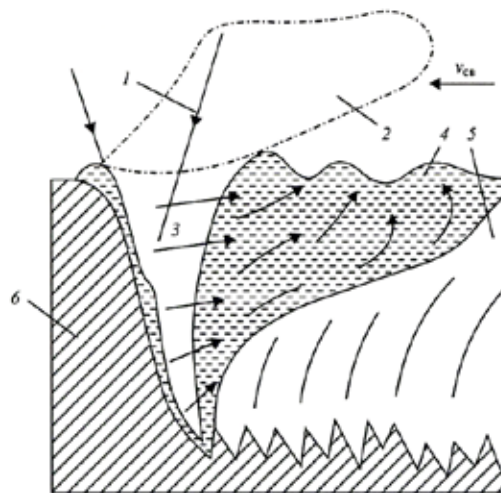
Схема продольного сечения сварочной ванны: 1 – лазерное излучение, 2 – плазменный факел, 3 – парогазовый канал, 4 – хвостовая часть сварочной ванны, 5 – закристаллизовавшийся металл, 6 – свариваемый материал
